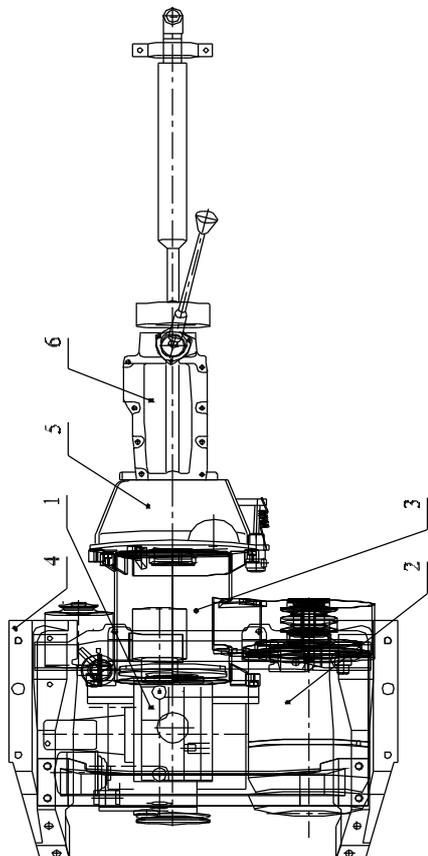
Конструкция КЭСУ ( 1 - ДВС ВАЗ-1111, 2 - электродвигатель (генератор), 3 - редуктор, 4 - рама энергетической установки, 5 - сцепление, 6 - коробка передач)
